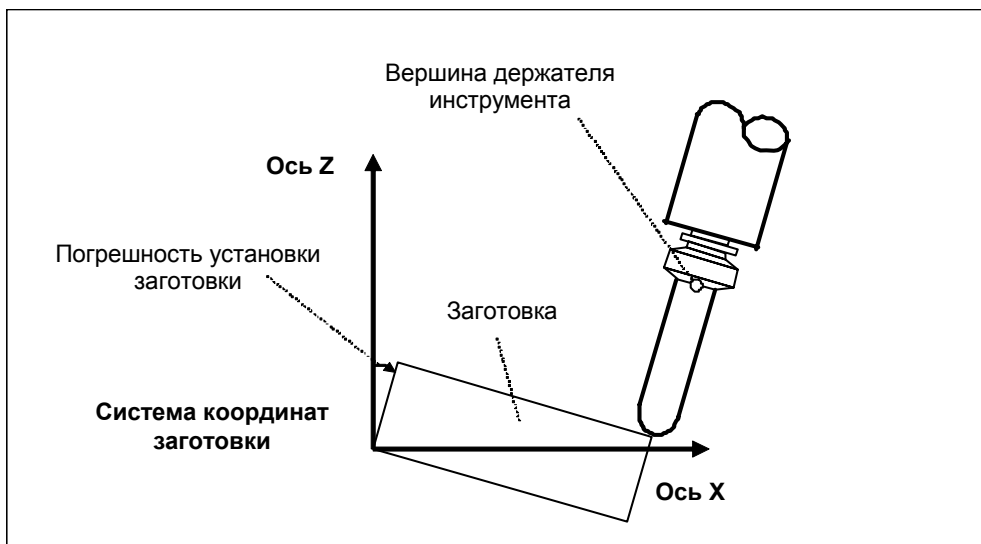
(j) Если присутствует погрешность установки заготовки (Если RCM=1)
